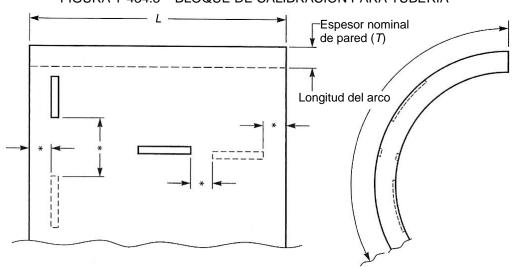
BLOQUE DE CALIBRACIÓN PARA TUBERÍA
